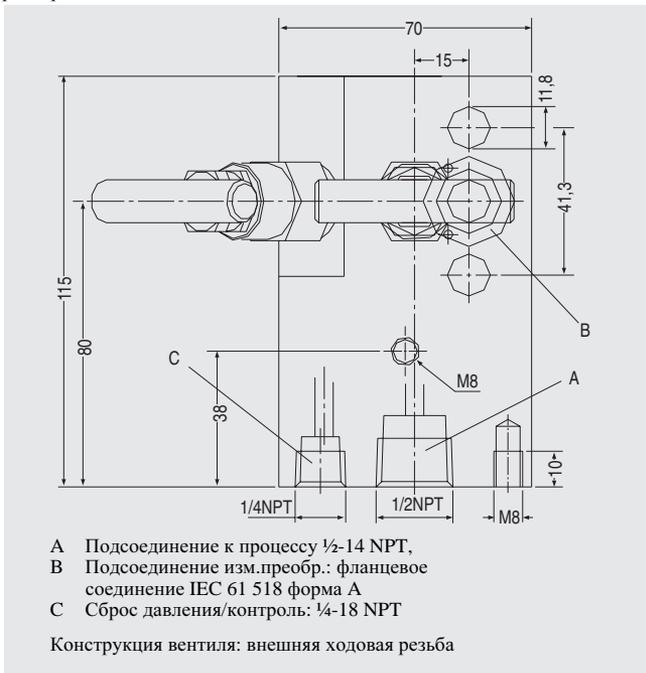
/108 Двухшпиндельный вентильный блок DN 5, размеры
